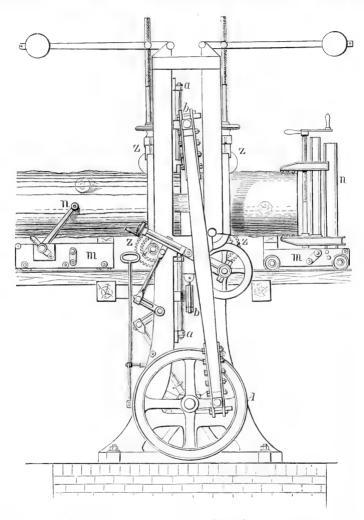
Ronftruttion einer Dampffage mit Bollgatter.
